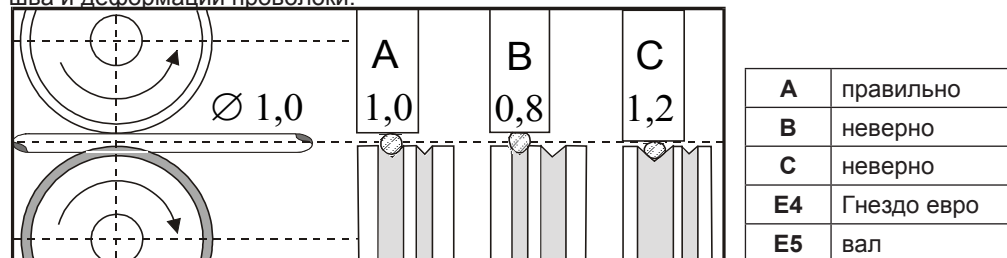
Влияние валков канавки на сварочной проволоки.
